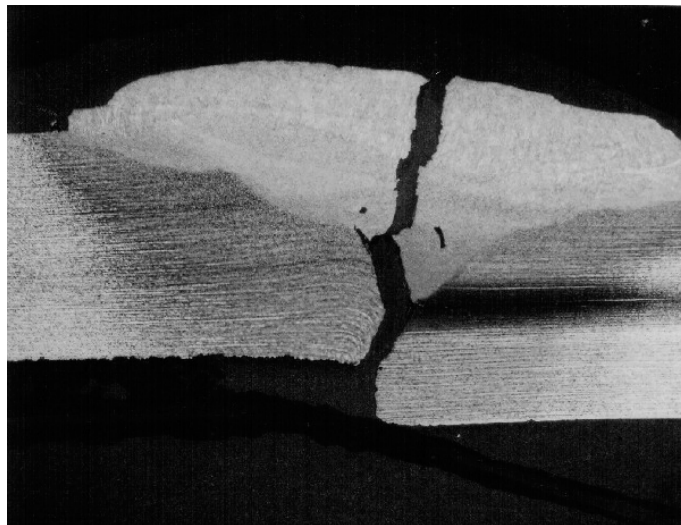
Fractura ocasionada por combinación de soldadura defectuosa y fatiga
